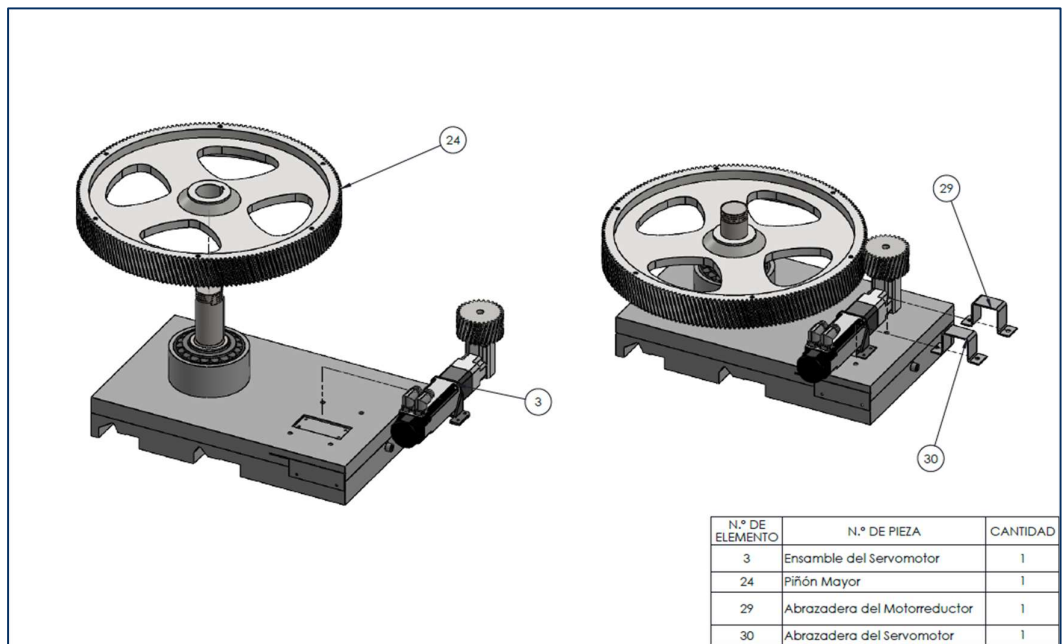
ensamble piñón mayor y servomotor subensamblado.
